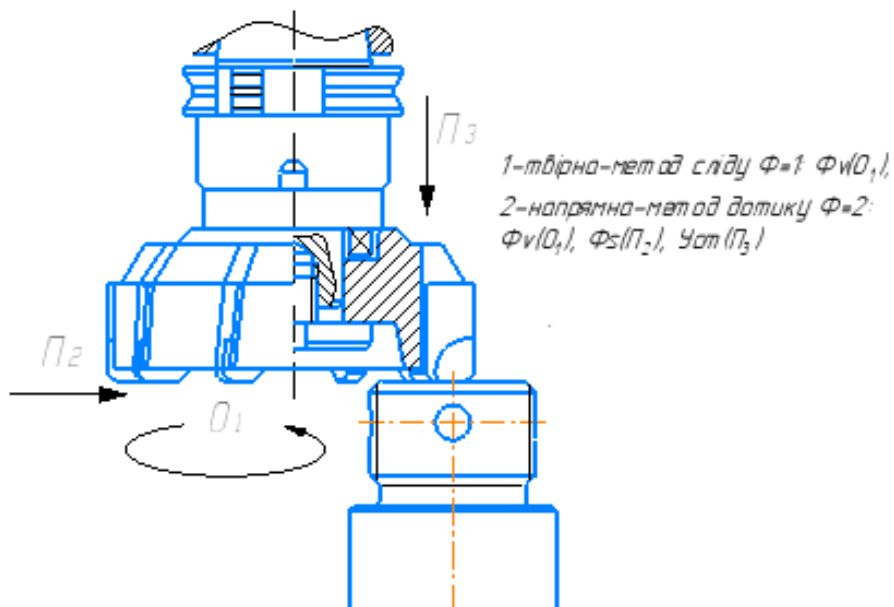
Схема формоутворення при фрезеруванні торцевою фрезою
